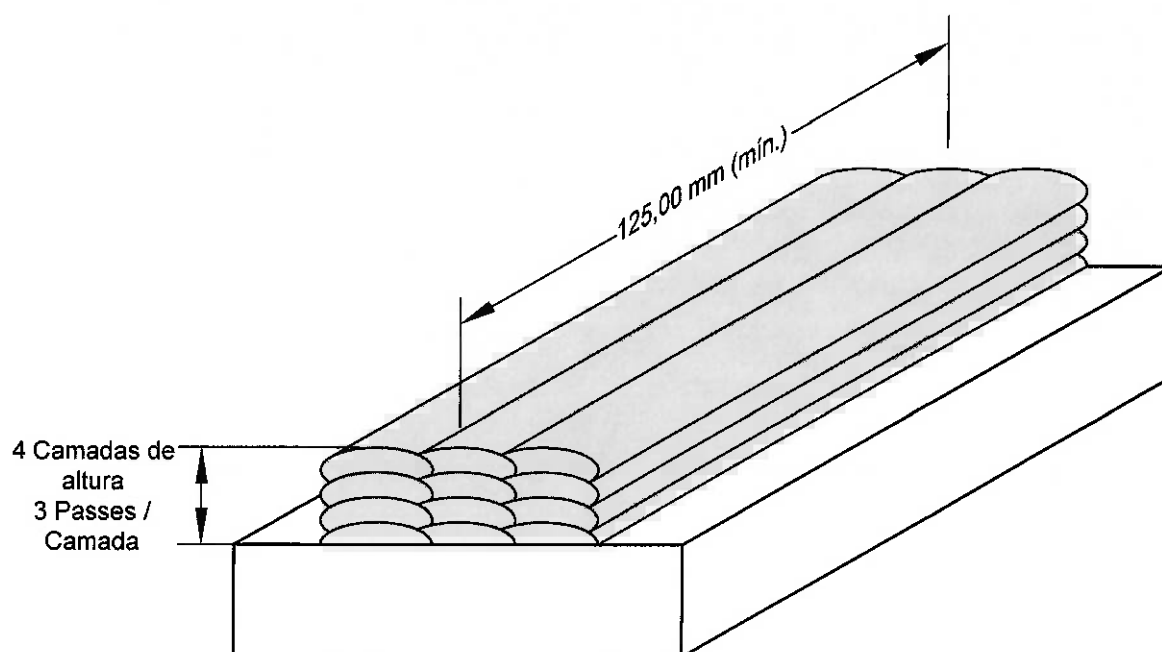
Corpo de prova (*weld pad*) para análise química do metal de solda [27].
